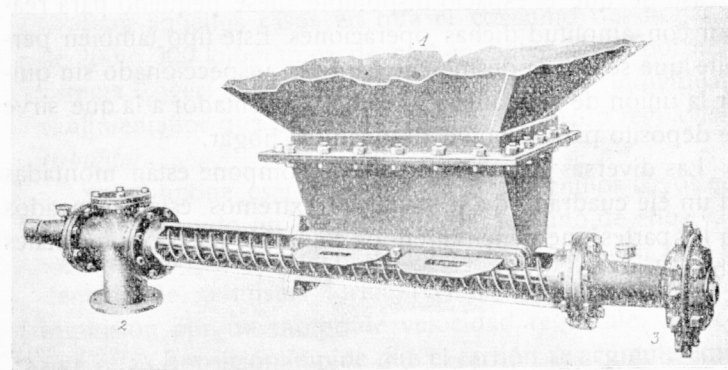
Alimentador Fuller de un solo cuerpo.
